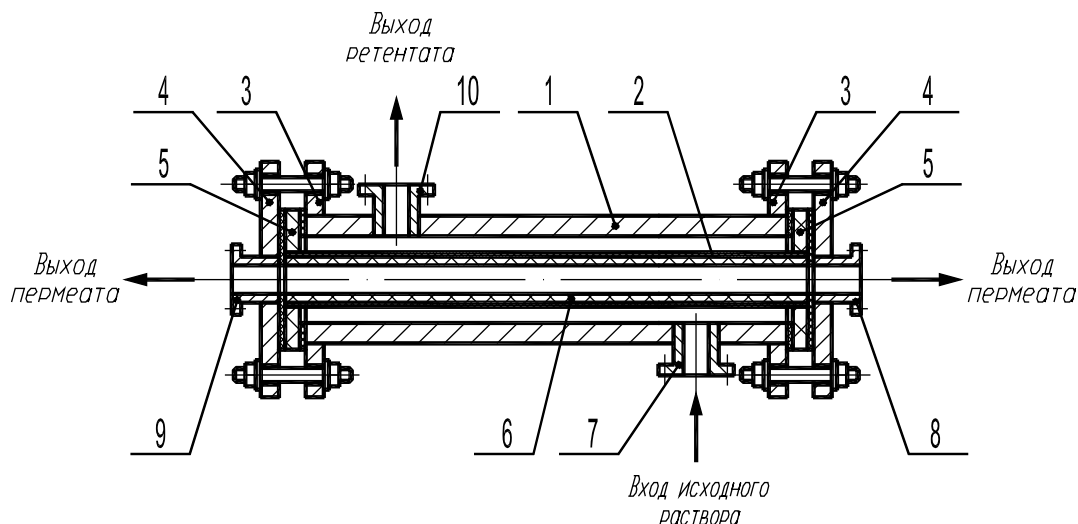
Схема мембранного модуля трубчатого типа. 1 — цилиндрический корпус; 2 — мембрана; 3,4 — фланцы; 5 — трубные решетки; 6 — пористая трубка; 7,8,9,10 — штуцера.
